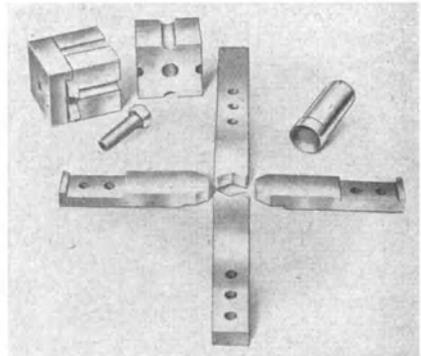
Werkzeuge zur Maschine Abb. 27.
